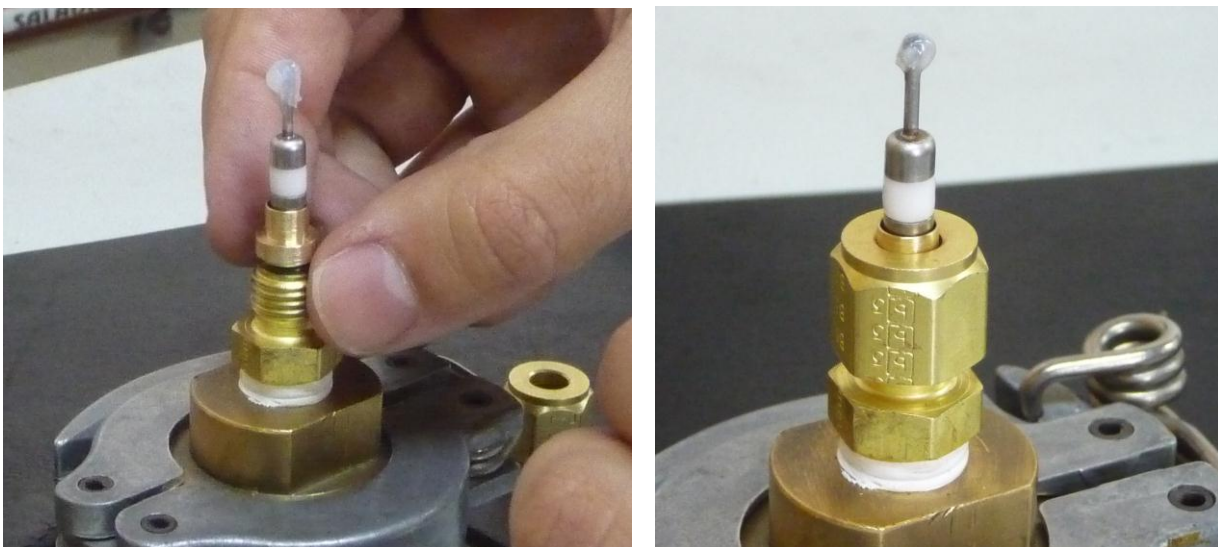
Preparación de la pieza para la prueba de estanqueidad de la soldadura láser
